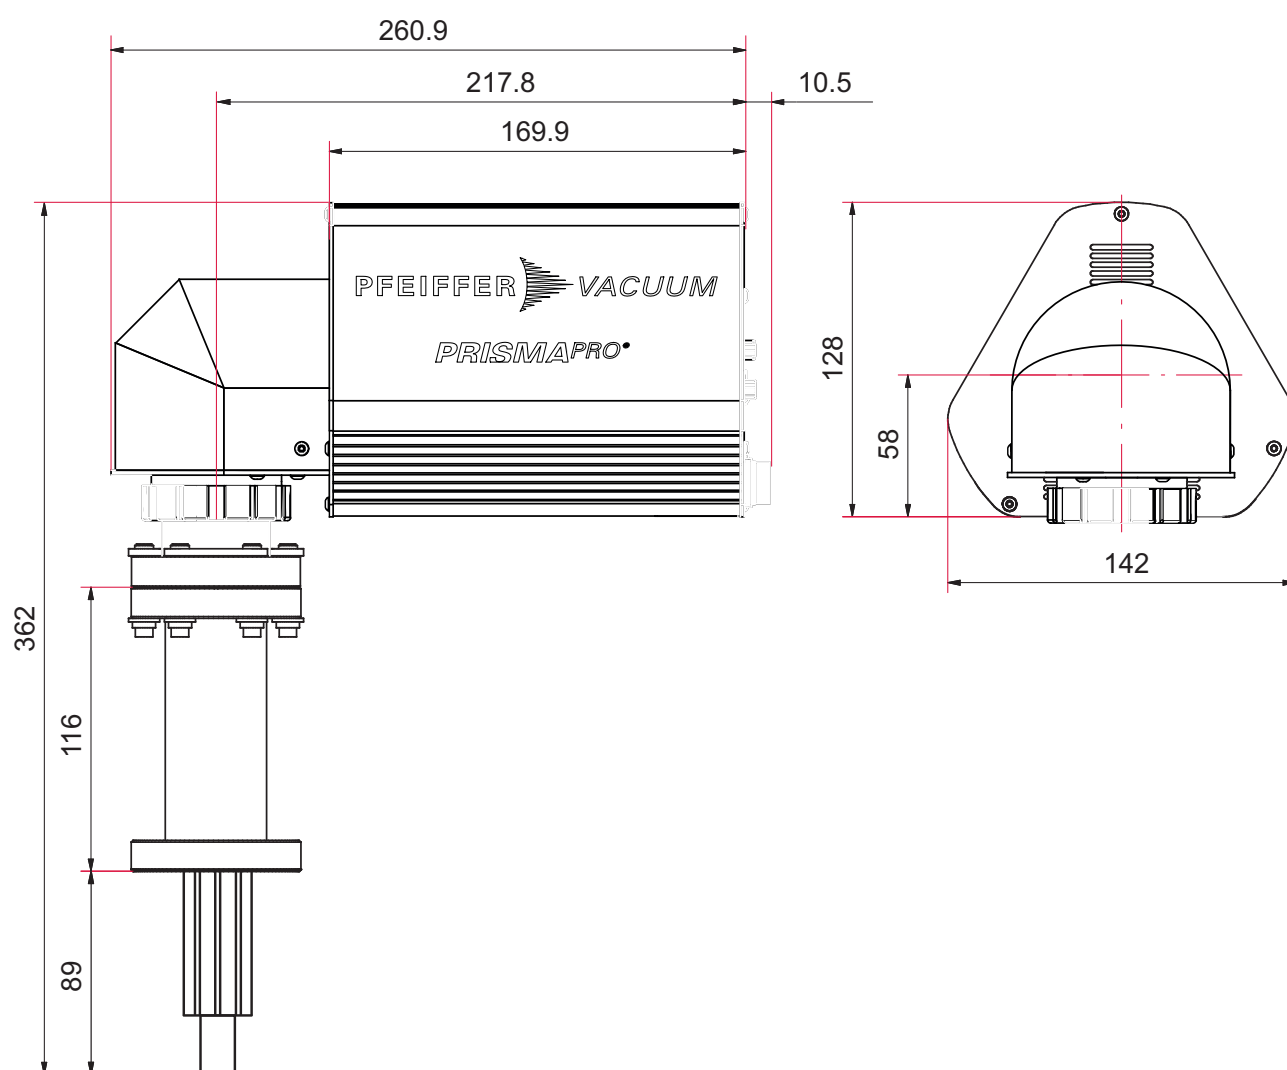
Dimensions QMG 250 M / SI à grille / QME 250 90°
